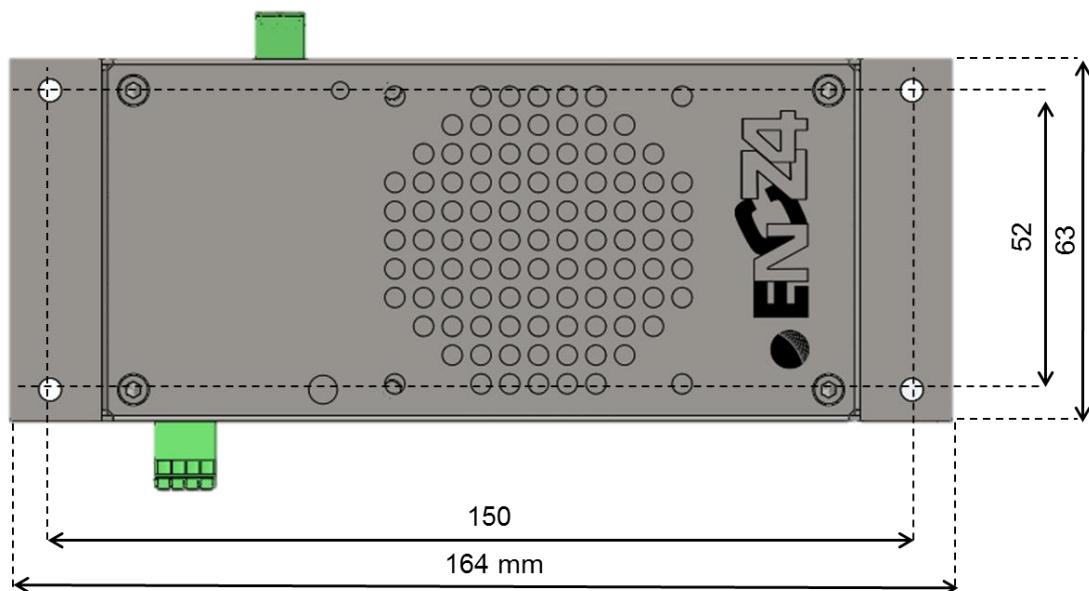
Dettaglio dei 4 fori di Ø 3,2mm per fissaggio apparato di elaborazione EnCZ4b
